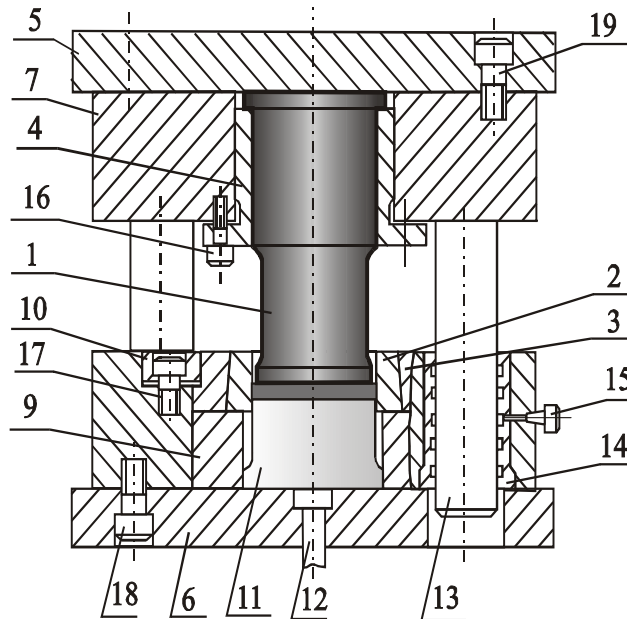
Схема штампа для осадки квадратної заготовки:
